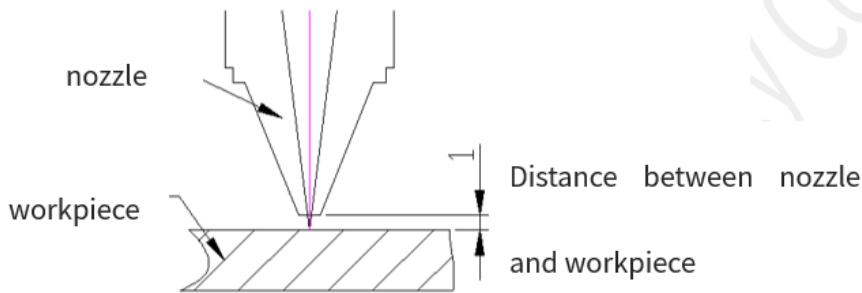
Distancia entre la boquilla y la pieza
